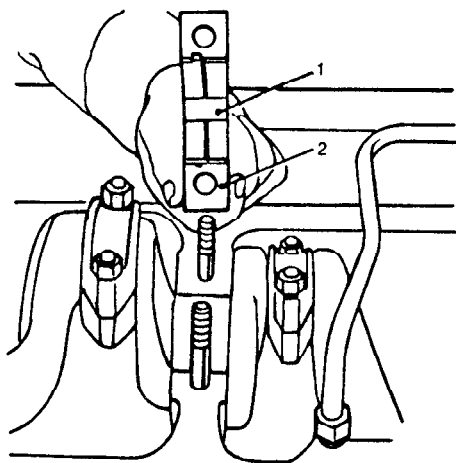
Comprobación de holgura de cojinete principal con calibrador de hojas: 1 calibrador de hojas, 2 tapa de cojinete
